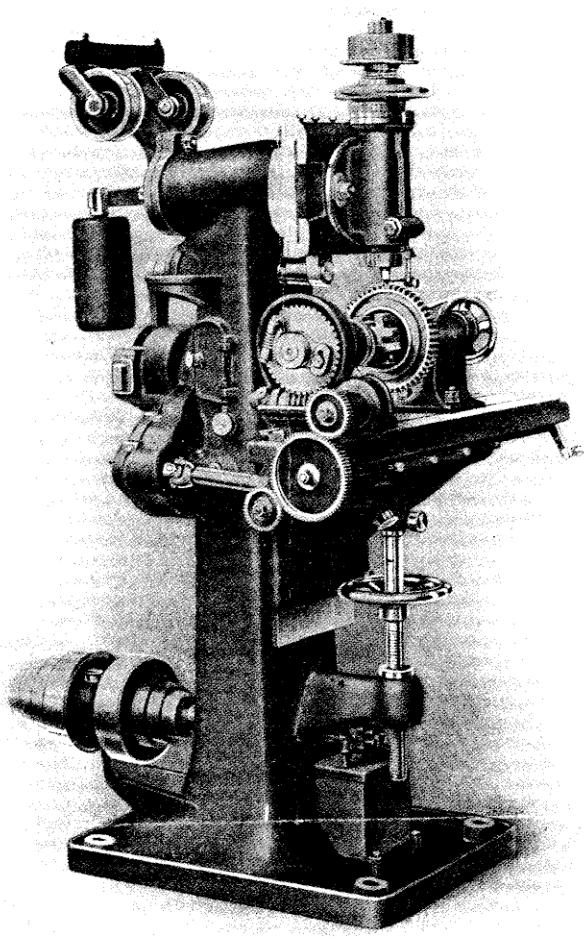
Machine automatique à arrondir les entrées de dents d'engrenages.
